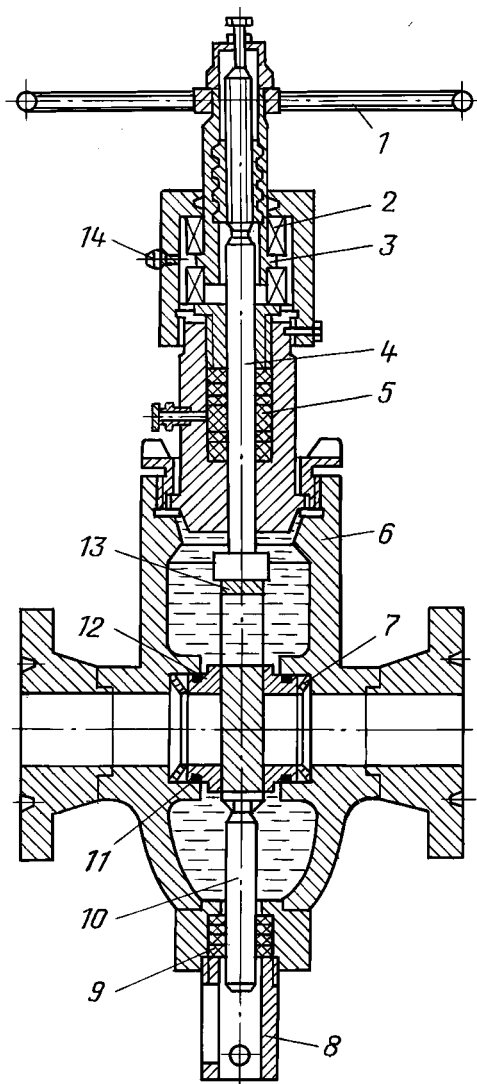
Задвижка с ручным управлением ЗМ-80×70
